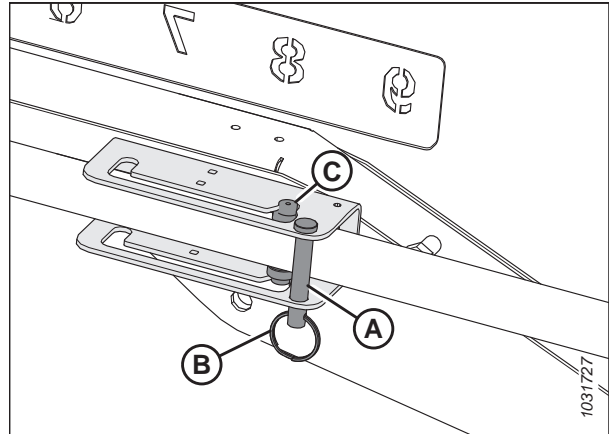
Regolazione del cilindro longitudinale tipo 2 – Posizione arretrata
